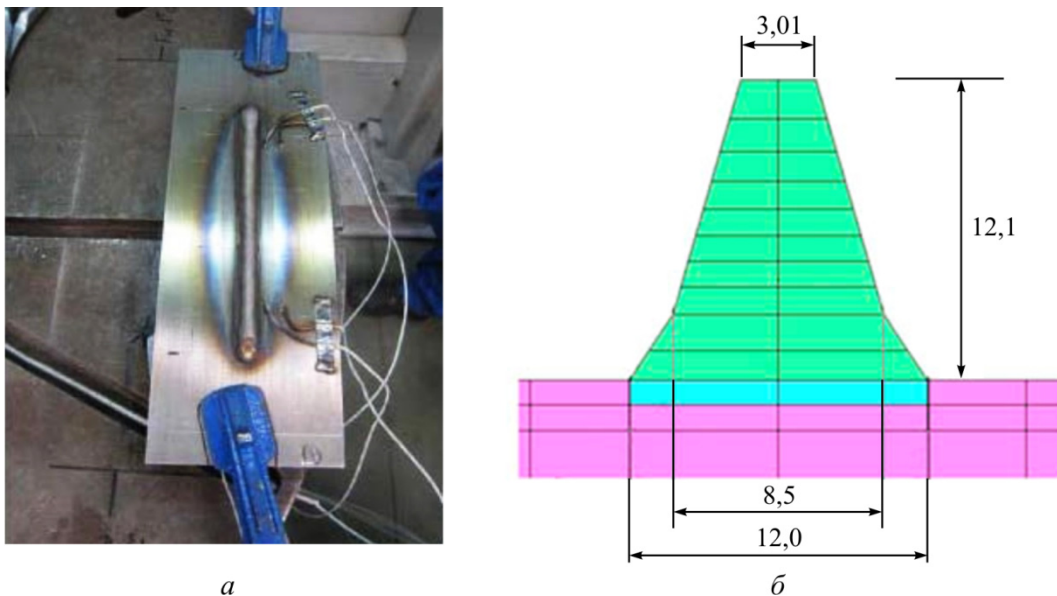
Общий вид изделия после эксперимента с системой креплений и датчиков (*а*); размеры наплавляемой зоны в сечении, мм (*б*) [33]
